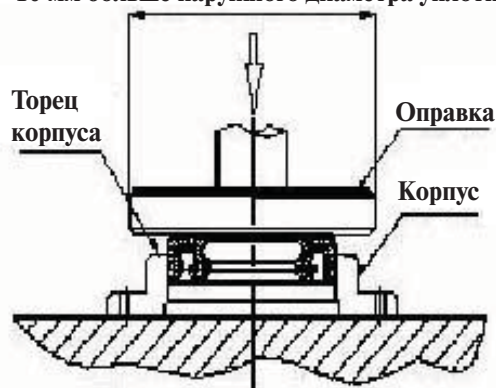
Установка манжеты с обеспечением параллельности манжеты и торца корпуса
